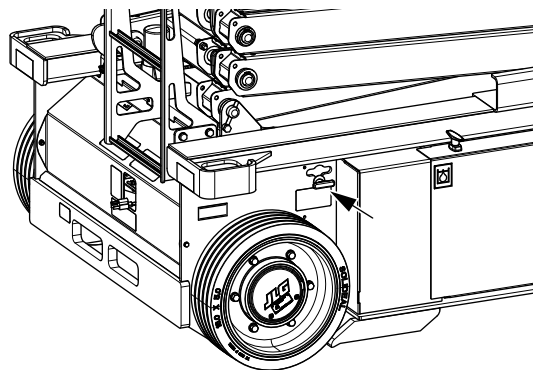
Placering av det manuella sänkingsreglaget (till höger baktill på maskinen – alla maskiner)
